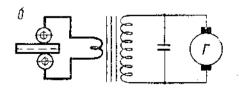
Схема промышленных способов сварки пластмаес токами высокой частоты;
